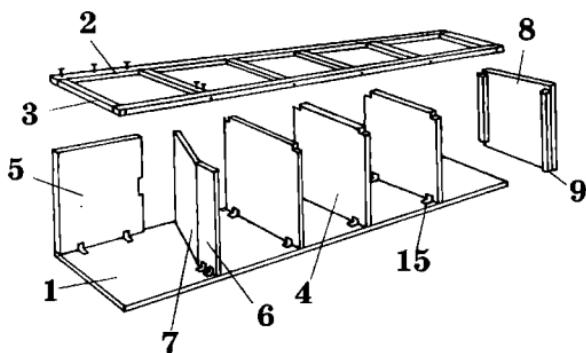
Сборка встроенного шкафчика для ванной комнаты (продолжение): 1 — боковина; 2 — бруск продольный; 3 — бруск поперечный; 4 — полка; 5 — фасадная плита; 6 — полка с откидной крышкой; 7 — откидная крышка; 8 — верхняя крышка; 9 — поперечина; 15 — уголок
